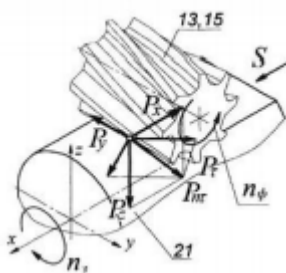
Силова схема взаємодії при зустрічному фрезеруванні
